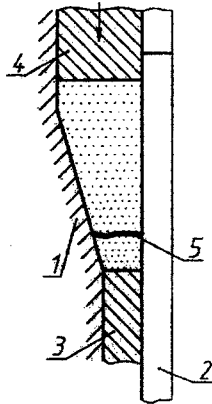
Вариант расположения порошковой детали в штампе: 1 - матрица; 2 - оправка; 3 - выталкиватель; 4 - пуансон; 5 - граница тромба
